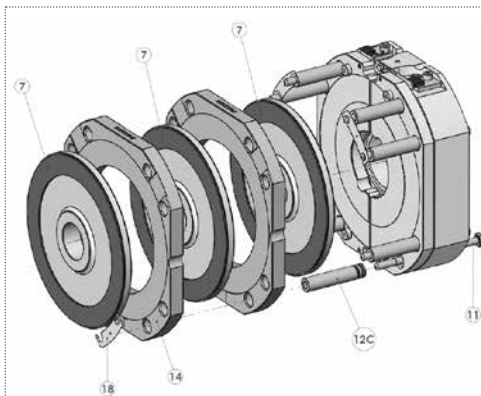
Vue éclatée du groupe bobine des freins DFX1.
